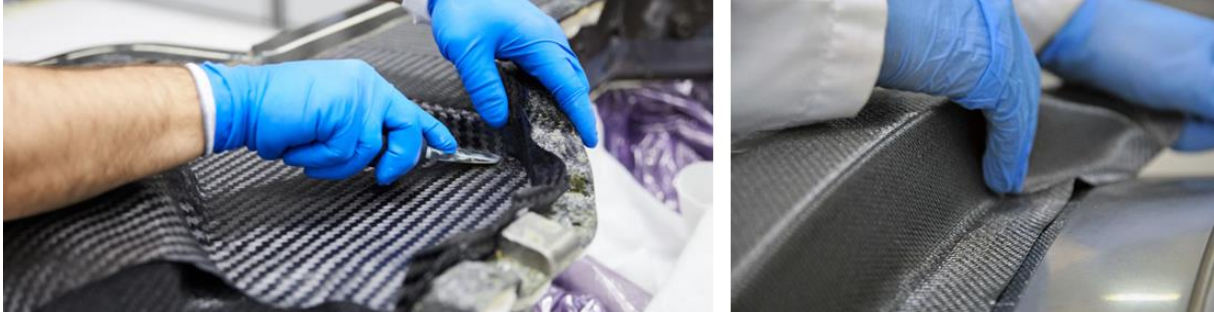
Obtention des pièces composites par drapage de pré-imprégnés⁶
